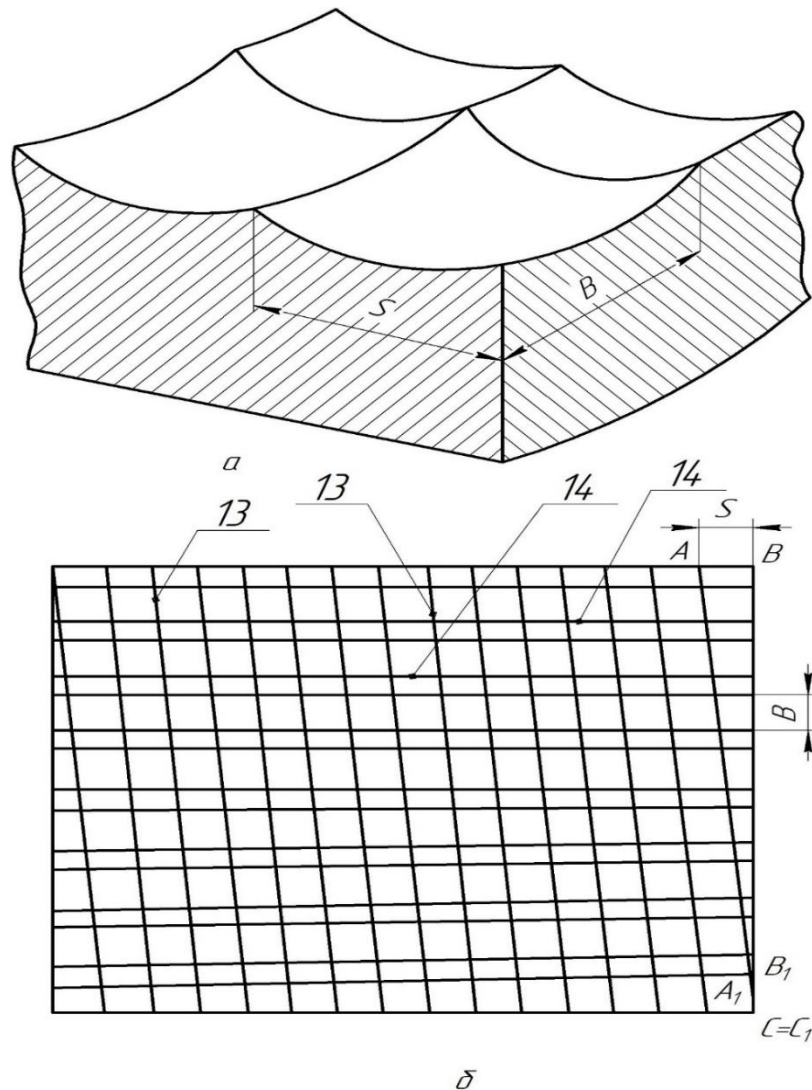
Фрагмент рельєфу поверхні деталі, обробленої протяжкою з фасонним деформуючим елементом і кульковою розкаткою (а) і розгортка циліндру внутрішньої поверхні отвору деталі, обробленої протягуванням і розкочуванням (б)
